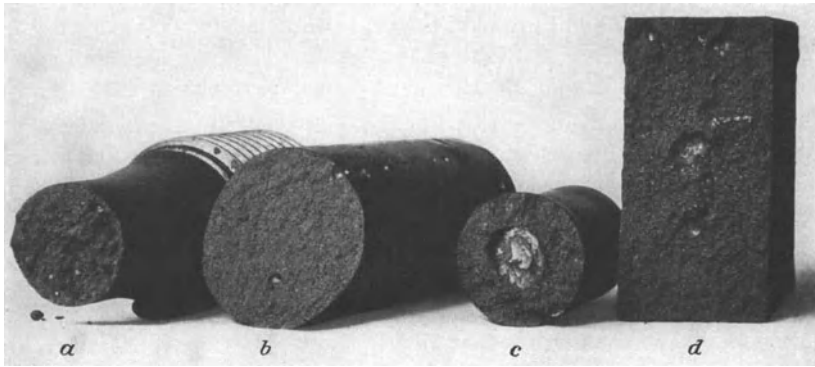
Versager von Gußeisenproben. *a* Zugprobe aus Maschinenguß mit vielen Schwitzkugeln. *b* Biegeprobe mit Gasblasen in der Mitte und der unbearbeiteten Oberfläche. *c* Zugprobe mit einer zentral gelegenen großen Schwitzkugel. *d* Vierkantbiegeprobe (nach British Standard) mit großen und kleinen Gasblasen.
